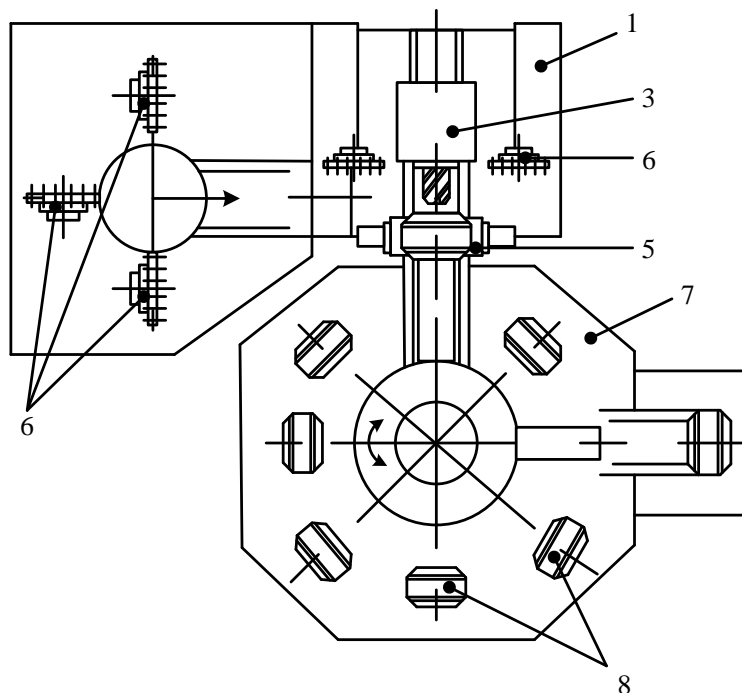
Компоновка гнучкого верстатного модуля фірми Heller
